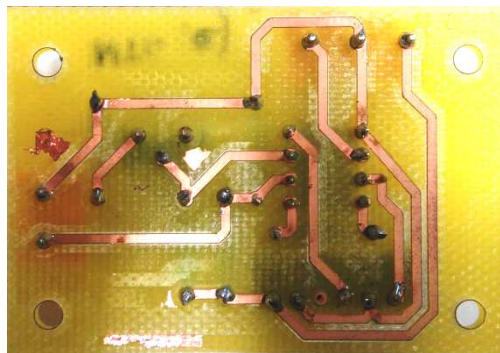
PARTE IMPRESA DE LA PCB PARA EL MÓDULO DE SENSADO MEDIANTE NTC
